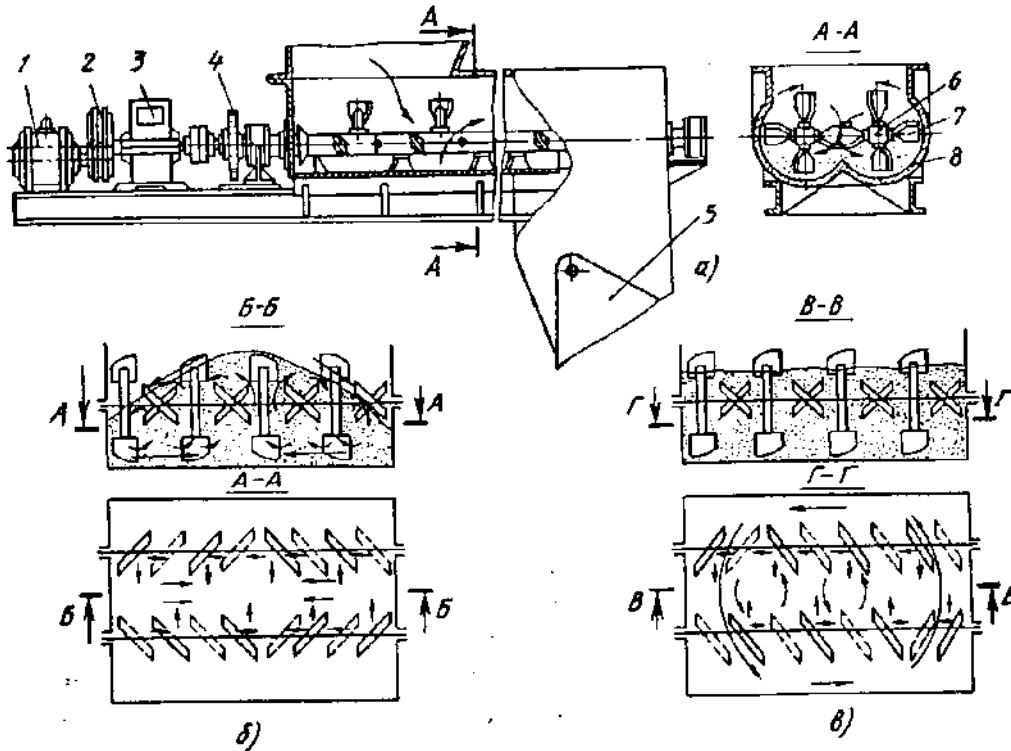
Двухвальный смеситель с горизонтальными валами непрерывного действия: *a* - схема смесителя; 1 - двигатель; 2 - клиноременная передача; 3 - редуктор; 4 - зубчатая передача; 5 - разгрузочный затвор; 6 - лопастные валы; 7 - лопасть; 8 - корыто смесителя. Схема движения смеси в корпусе смесителя: *б* - противоточная; *в* - поточно-контурная
